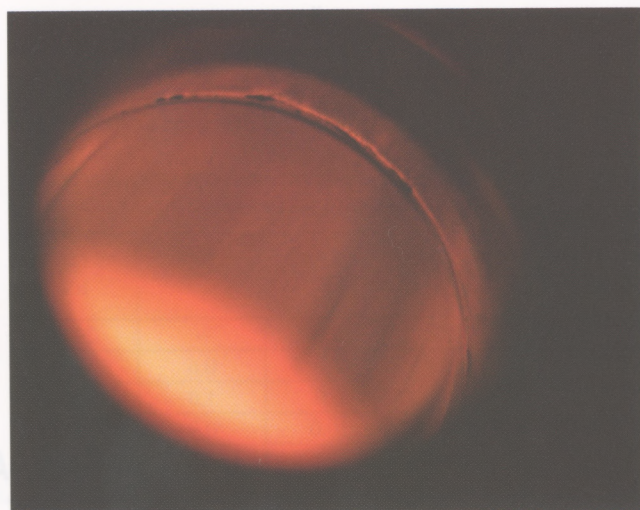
Сплав YL05.1, волока-заготовка 16×13 мм (диаметр 1,77 мм), отработала 71 ч, поперечная трещина по кольцу износа с выкрашиванием твердого сплава
